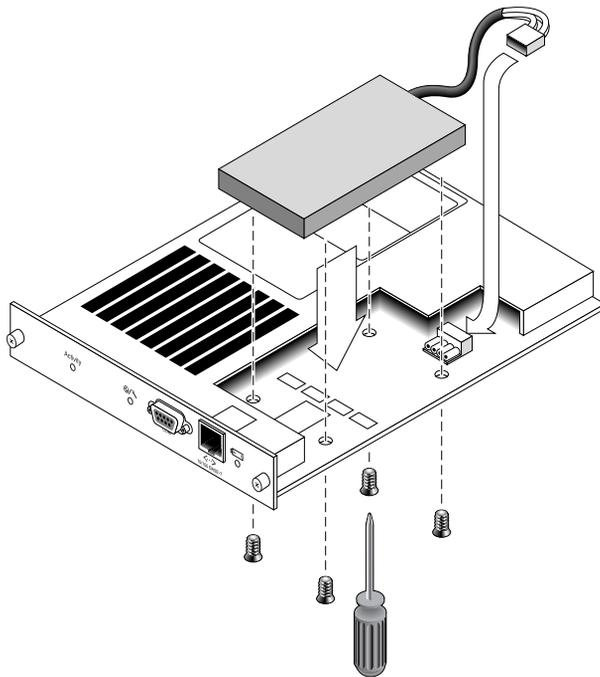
Vue du haut et de côté du module du contrôleur pendant le remplacement de la batterie
